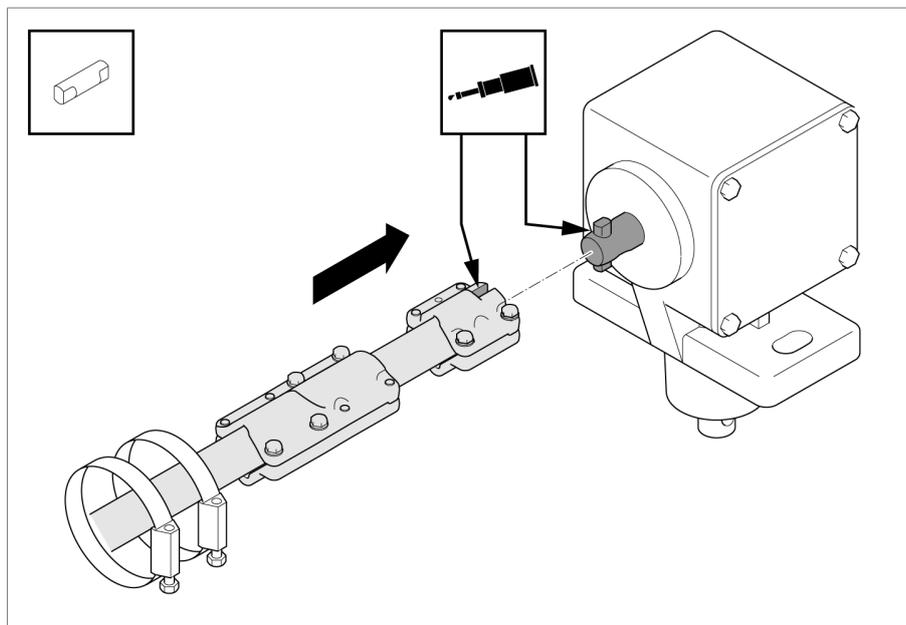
Glissez le tube carré avec la pièce d'accouplement sur l'extrémité d'arbre
